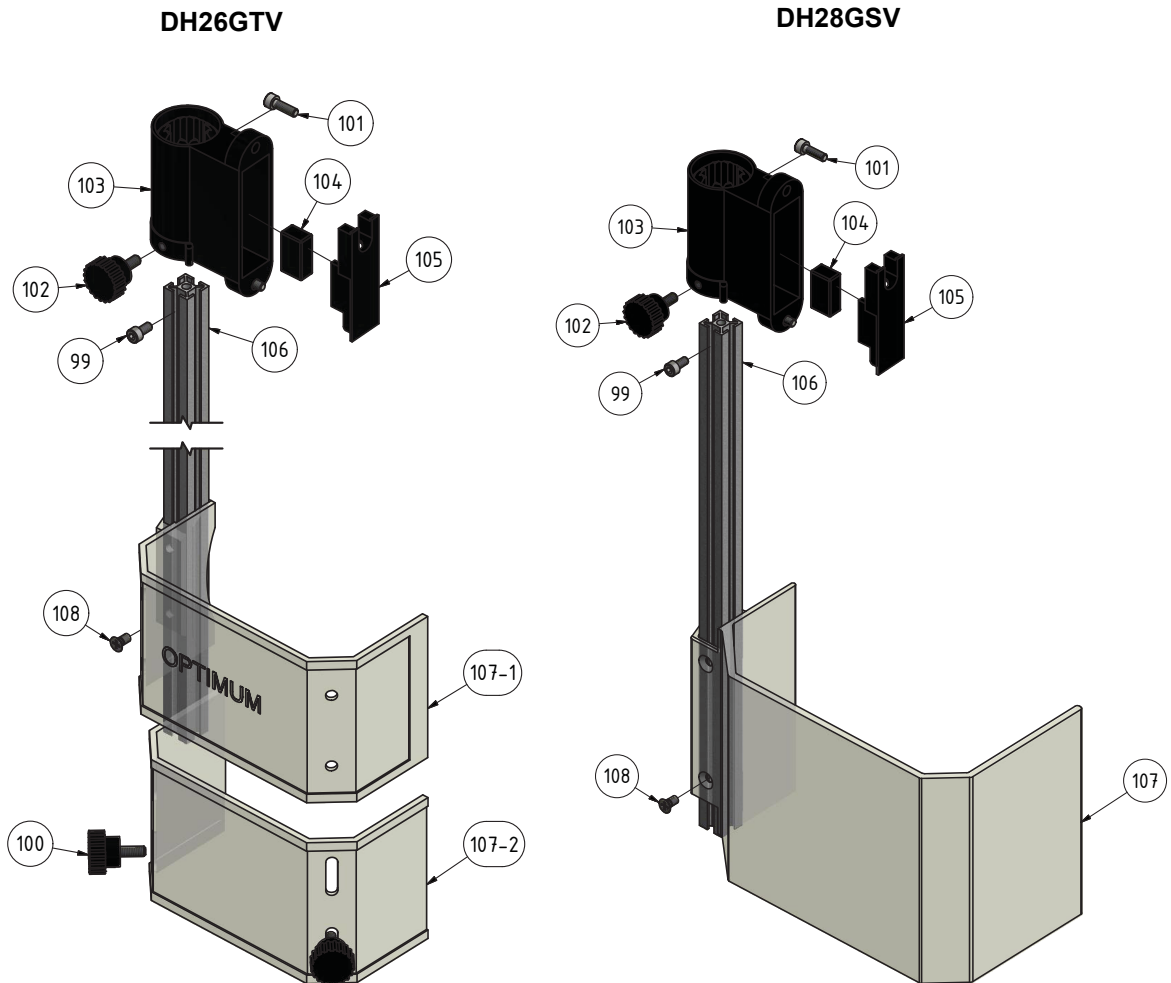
Bohrfutterschutz- Drilling chuck protection
